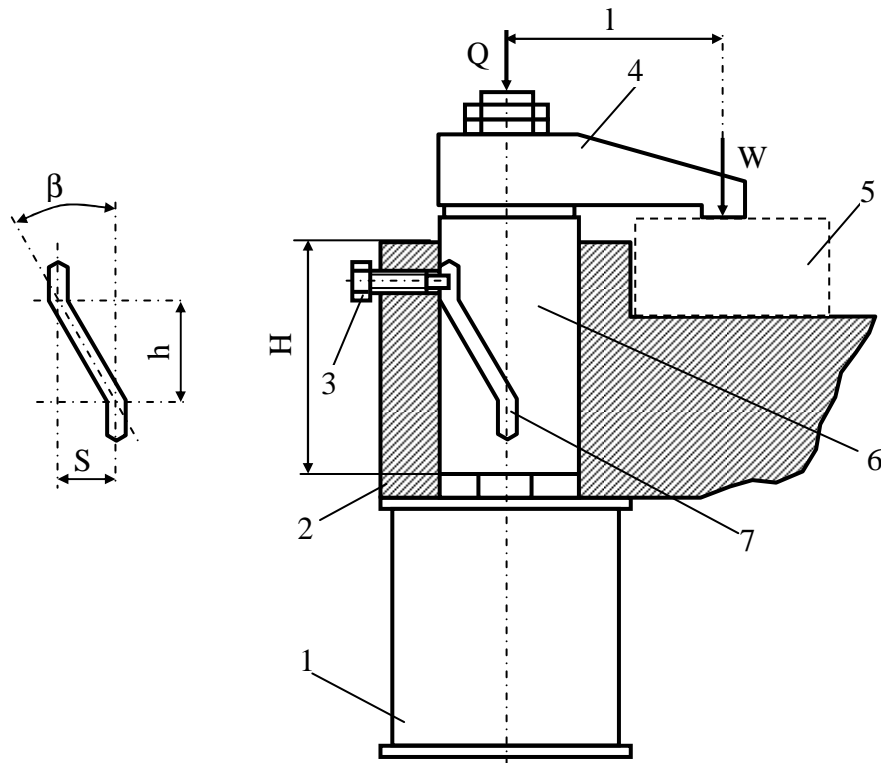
Схема Г-подібного прихвата з пневмоциліндром:
